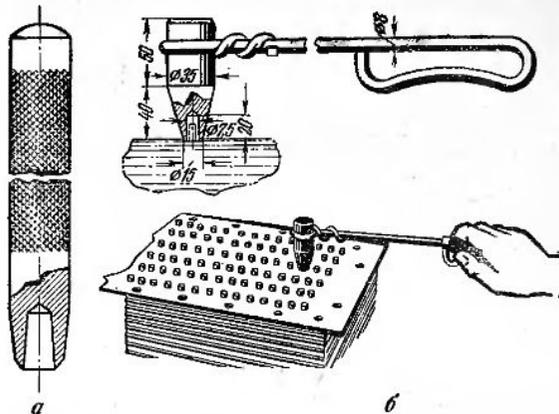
Инструменты для установки новых трубок в сердцевину радиатора:
